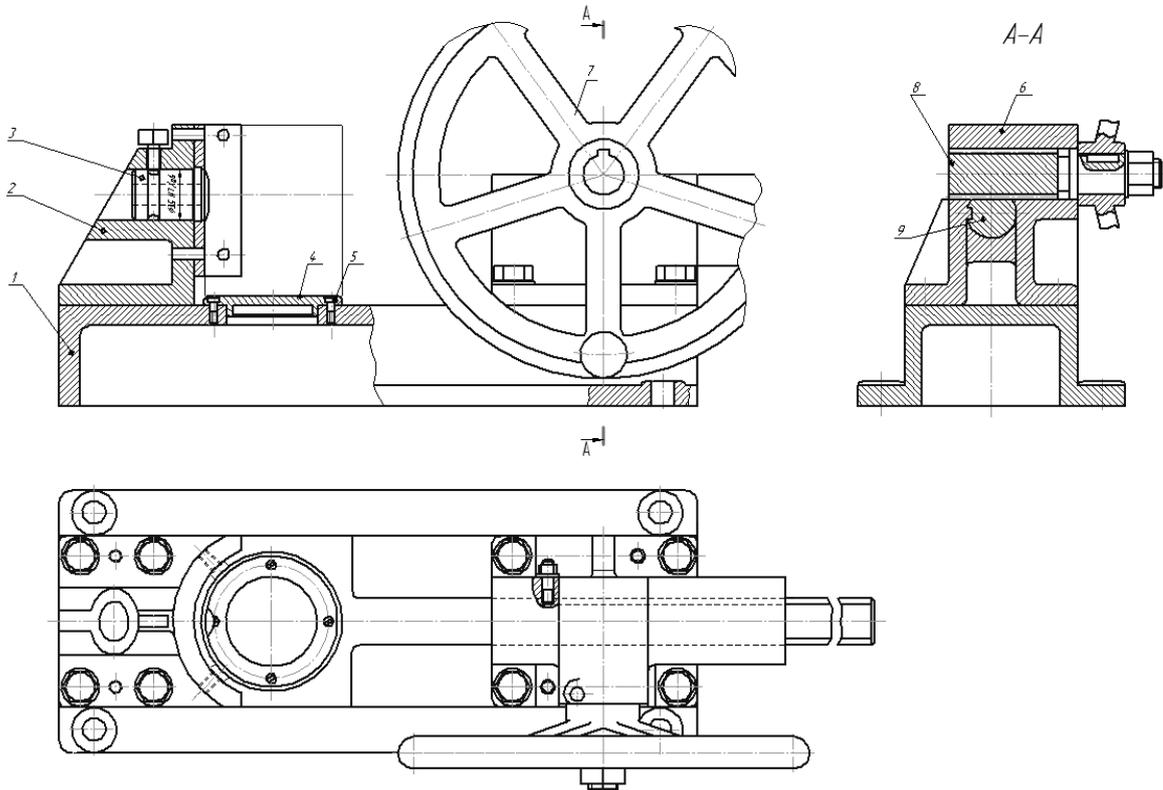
Приспособление для запрессовки и выпрессовки поршневого пальца
